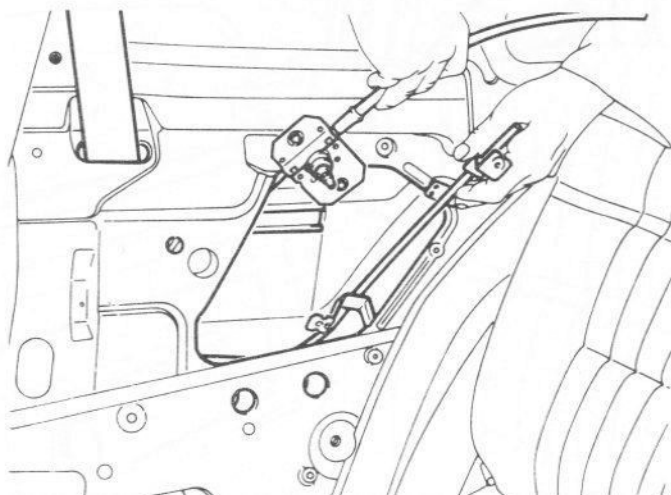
Dépose du lève-glace arrière – modèles Cabriolet (Sec 21)
